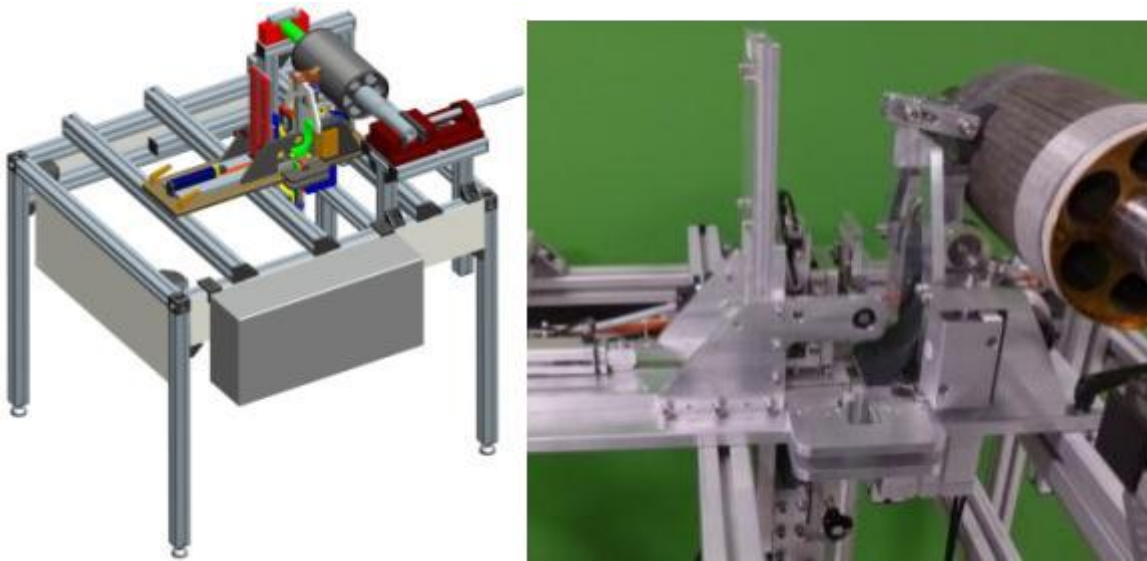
CAD-Modell (links) und realer Aufbau (rechts) des Demonstrators für Rotoren mit oberflächenbestückten Magneten
